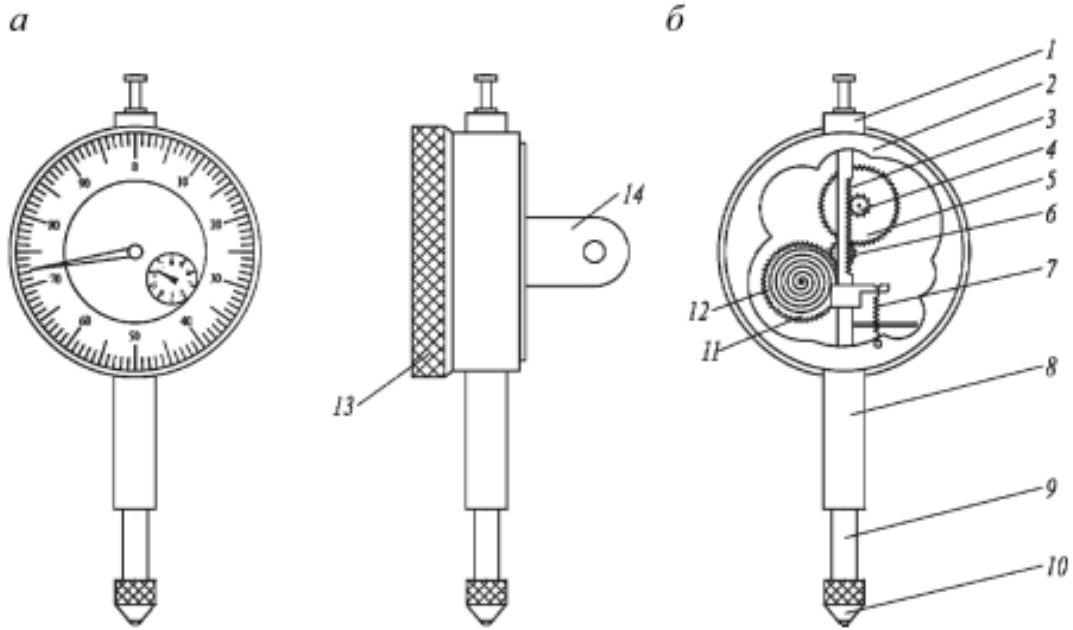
Індикатор годинникового типу ИЧ-10: а - загальний вигляд; б - основні частини індикатора: 1, 8 - верхня і нижня гільзи (виконують роль напрямних для переміщення вимірювального стрижня); 2 - кільце; 3 - зуби для середньої частини вимірювального стрижня; 4 - трібка; 5 - зубчасте колесо (жорстко пов'язане з трібкою); 6 - шестерня (на осі якої насаджена велика стрілка індикатора); 7 - пружина (для утримування вимірювального стрижня в нижньому положенні); 9 - вимірювальний стрижень; 10 - наконечник; 11 - зубчасте колесо; 12 - спіральна пружина (передає через зубчасту передачу зусилля, утримує вимірювальний стрижень в нижньому положенні); 13 - поворотне кільце (за допомогою кільця прилад можна налаштувати на «нульовий» або будь-який інший, за бажанням оператора, відлік), 14 - хвостовик (для прикріплення індикатора до струбцині).
